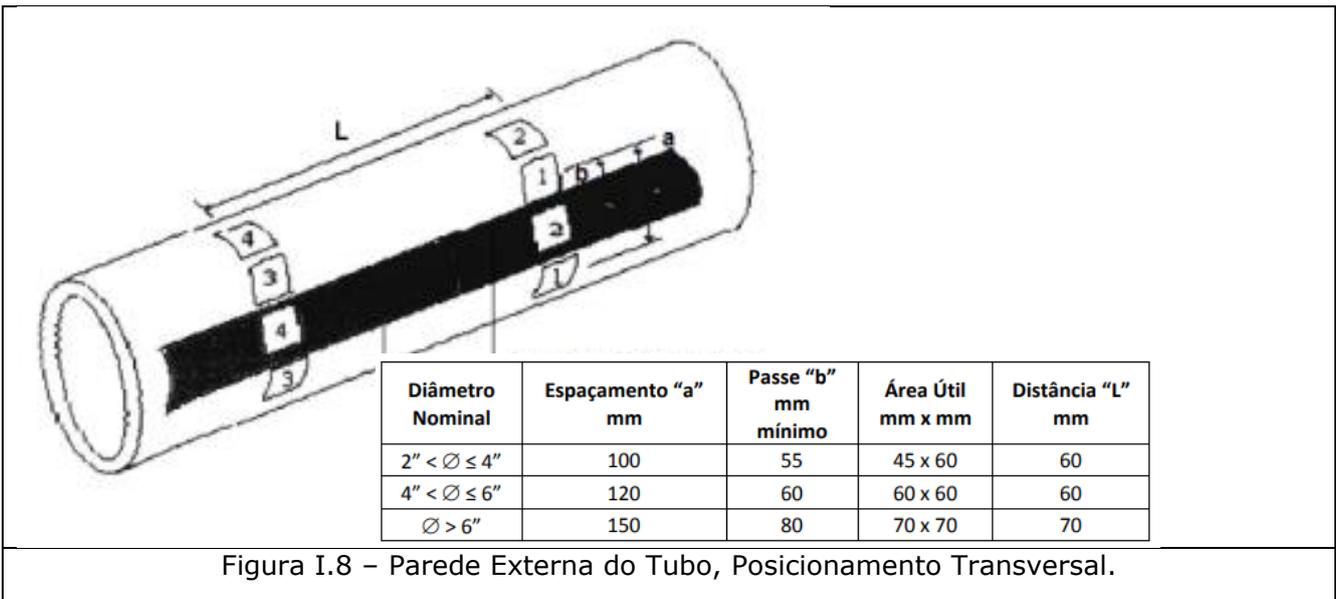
Parede Externa do Tubo, Posicionamento Transversal.
